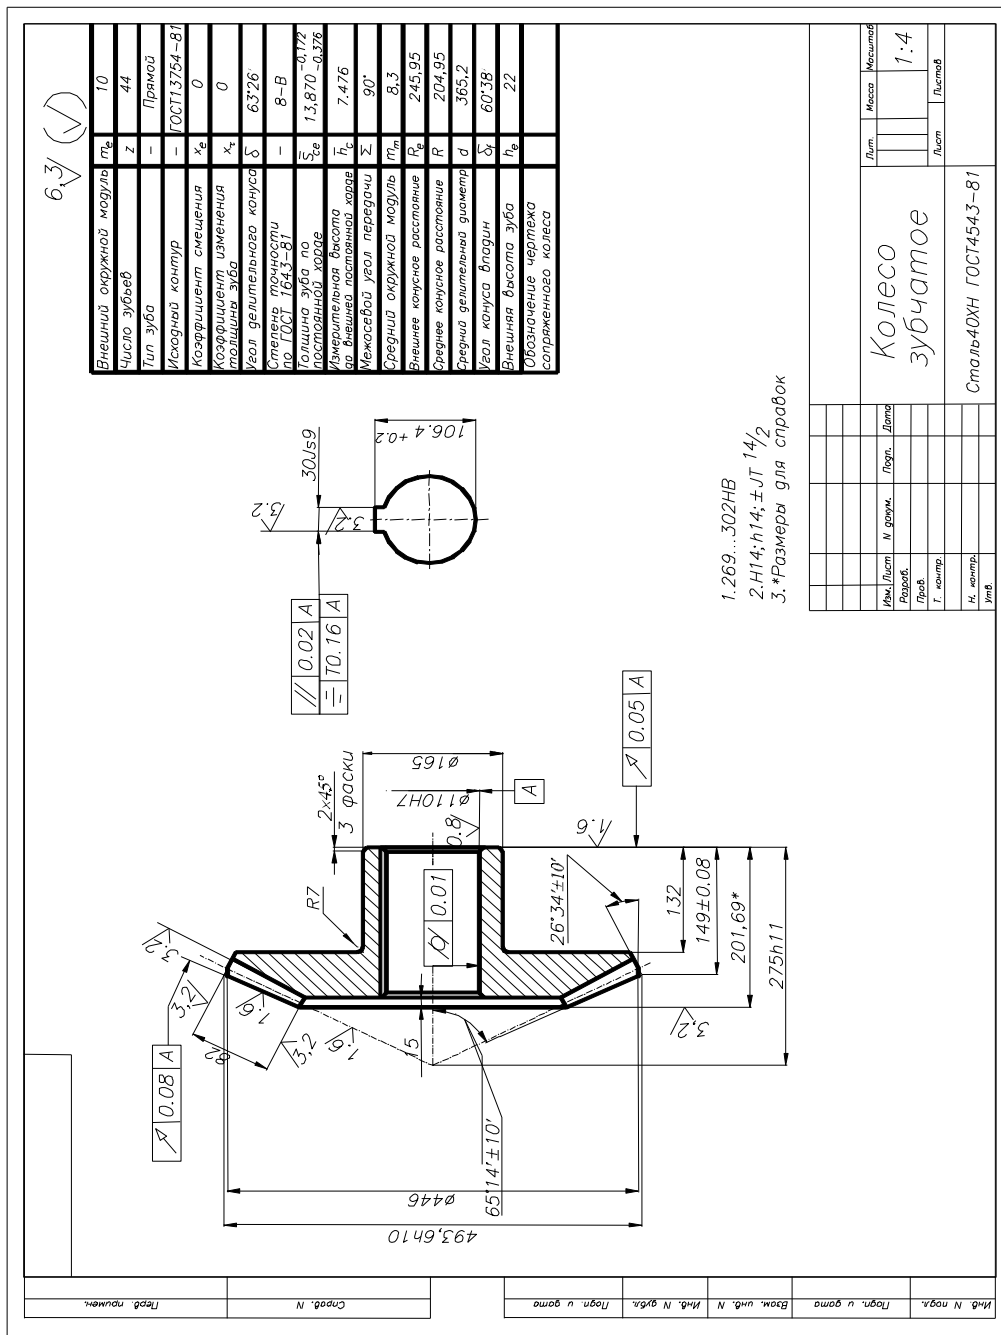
Рабочий чертёж колеса конического прямозубого
